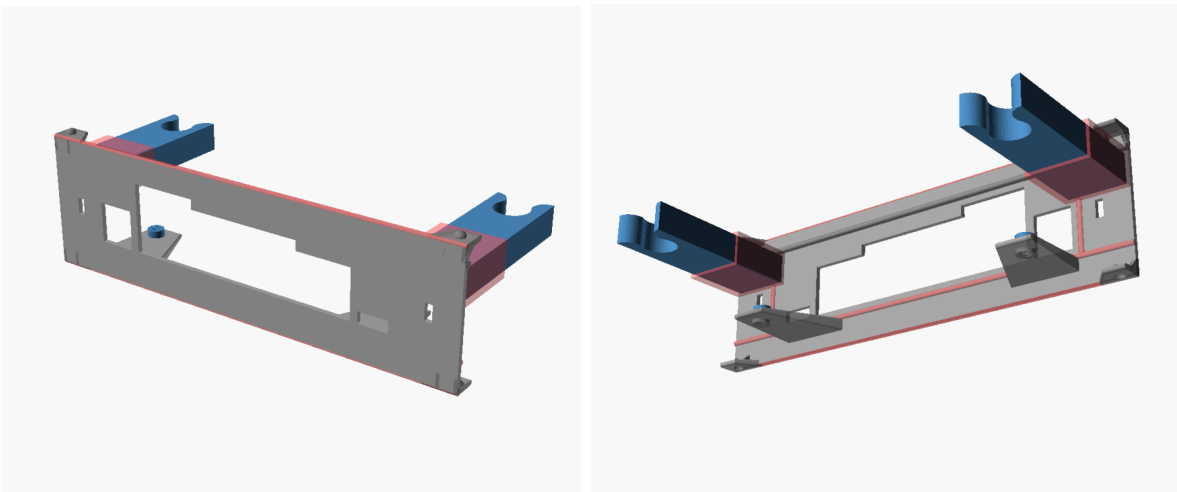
Vista frontal y trasera del soporte 3D diseñado.
